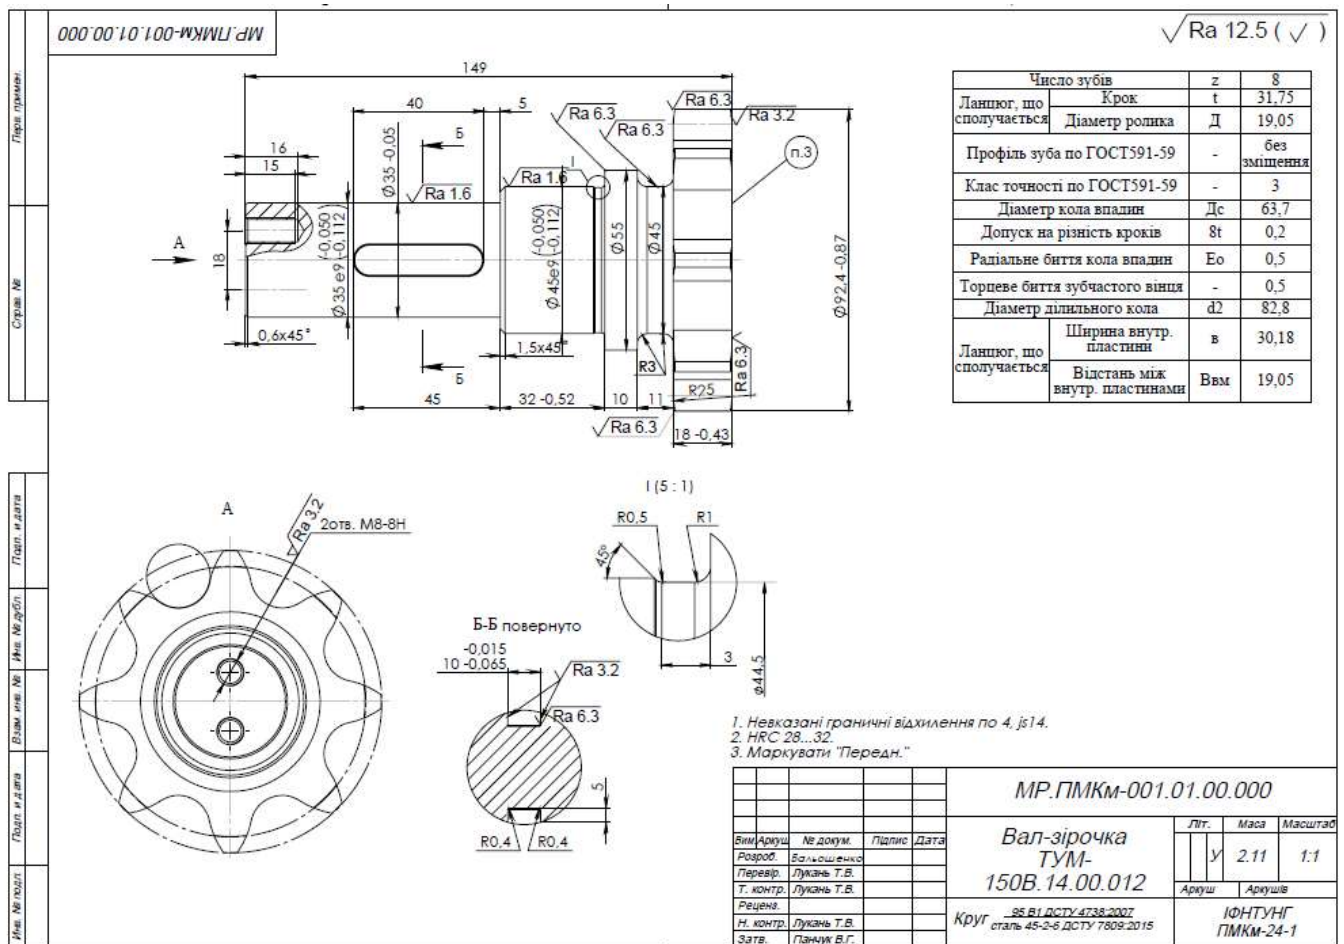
Креслення деталі Вал-зірочка «ТУМ-150В.14.00.012
